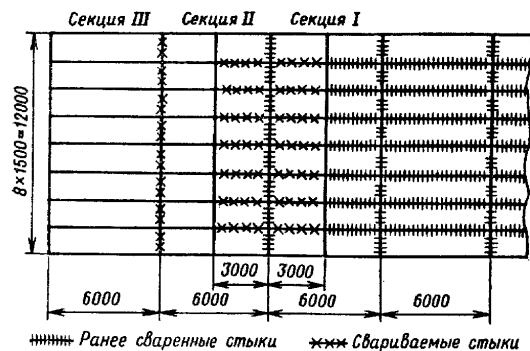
Расположение соединений и последовательность сварки на двухъярусной установке
